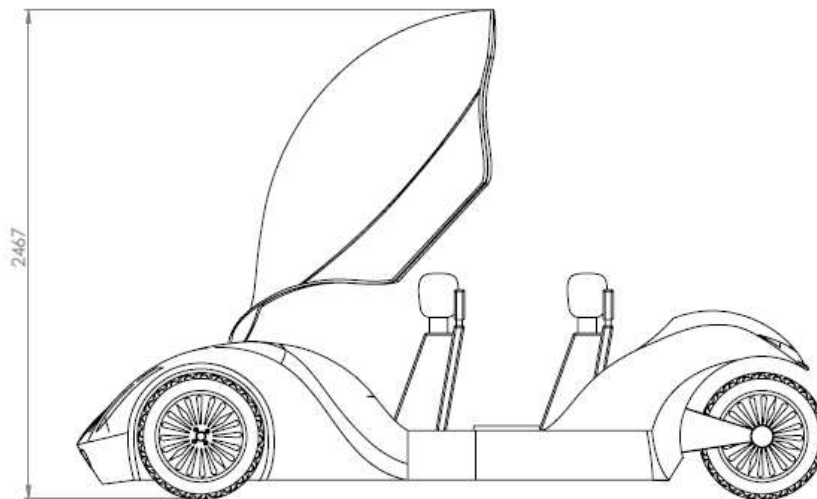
Viser taket hevet i front, sett fra siden skrått bakfra
